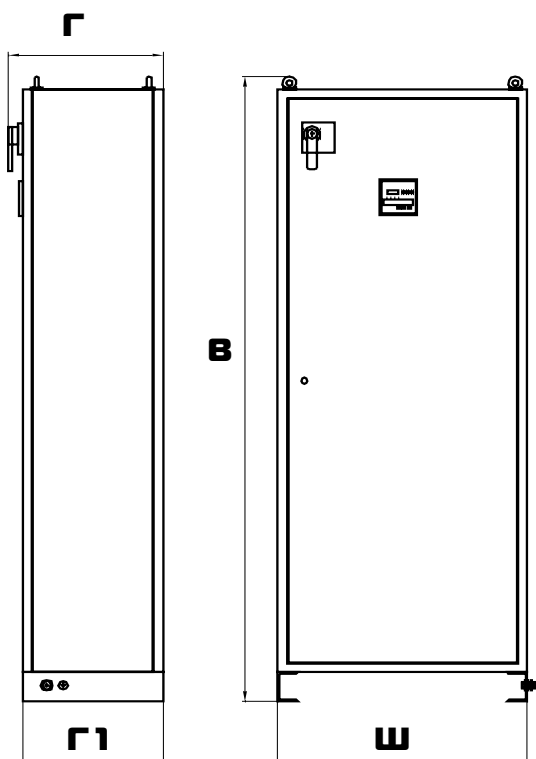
Габаритный чертеж КРМ-0,4 (50-200 кВАр) IP54
